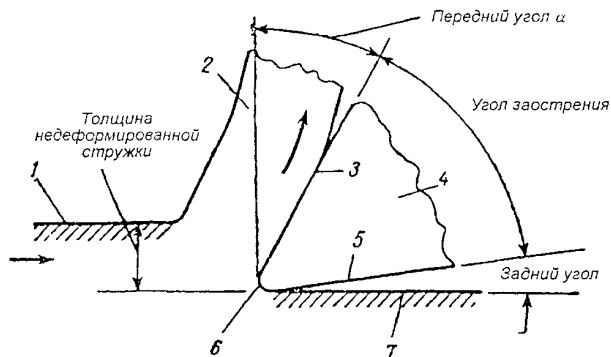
Основные элементы резца. 1 – обрабатываемая деталь; 2 – стружка;
